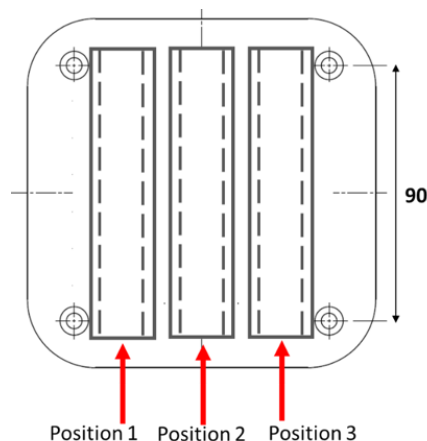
Schéma des positions des éprouvettes de fatigue sur le plateau de fabrication SLM pour la fabrication des revêtements : configuration pour 3 éprouvettes par fabrication
